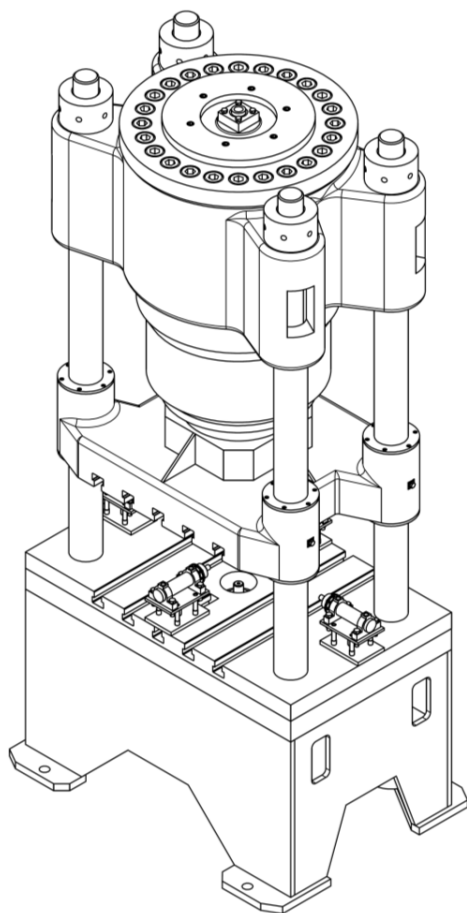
Месторасположение главного цилиндра гидравлического пресса
